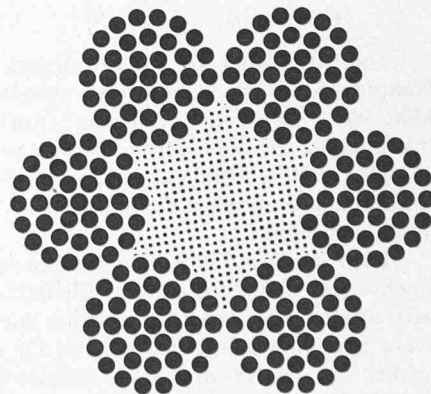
Querschnitt des untersuchten Seiltyps von 90 mm Durchmesser
